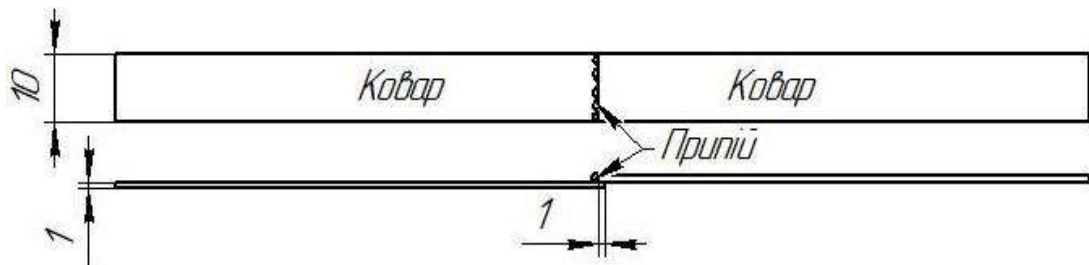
Схема зразків Ковар – Ковар для механічних випробувань
